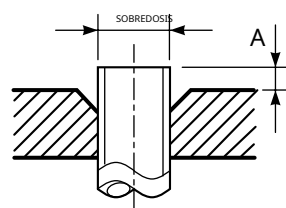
Dimensiones de procesamiento de abocardado
